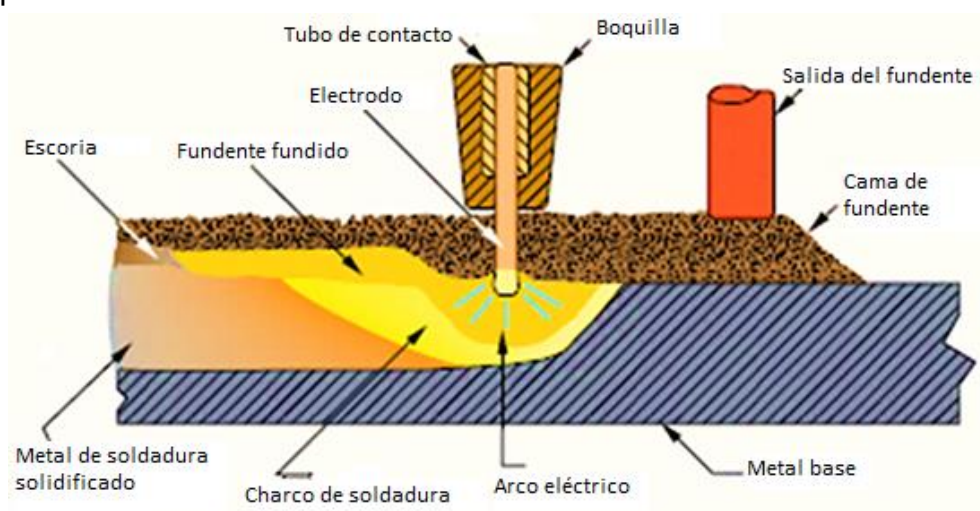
Esquema del proceso de soldadura por arco sumergido, SAW [29].
